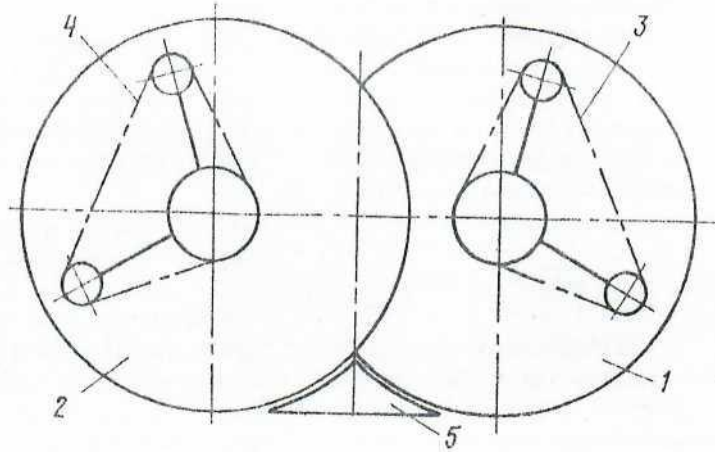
Схема викопувального пристрою [14], загальний вид
